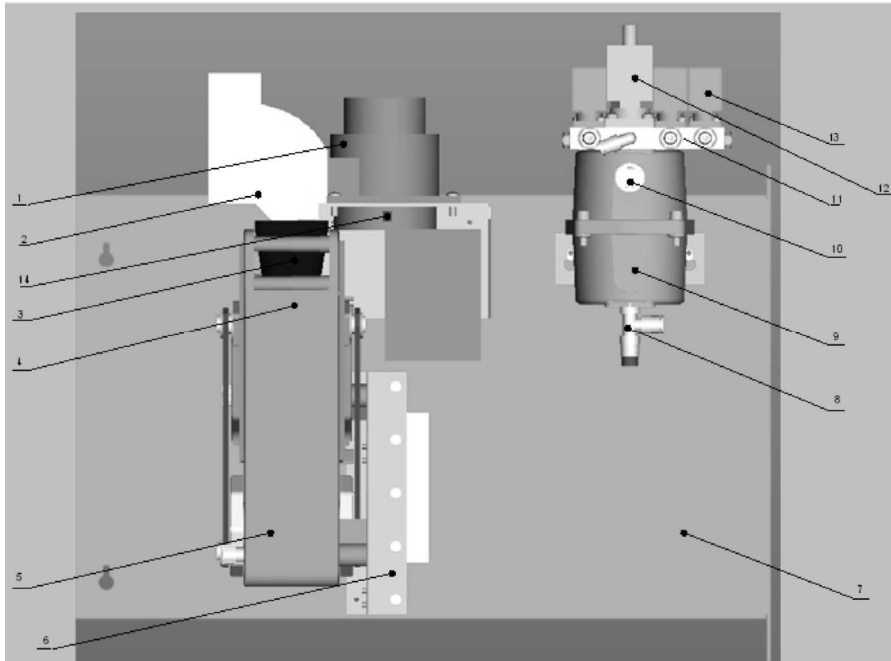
Блок приготування заварної кави: 1 – кавомолка; 2 – дозатор кави; 3 – жолоб для подачі кави; 4 – отвір для подачі гарячої води під натиском; 5 – брівер; 6 – редуктор; 7 – кронштейн кріплення; 8 – заглушка; 9 – корпус бойлера; 10 – датчик температури; 11 – розподільник клапанів; 12, 13 – електроклапани; 14 – регулятор помелу
